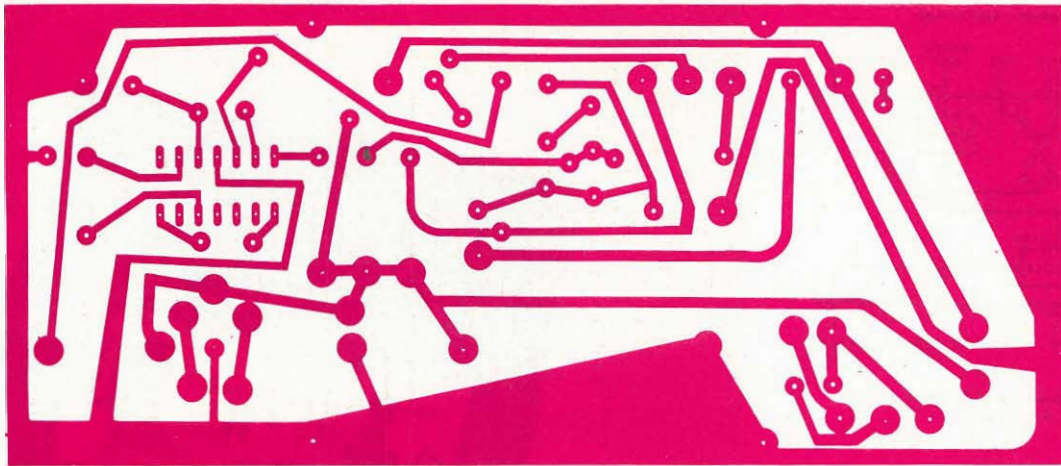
Basetta vista dal lato rame in scala 1:1.
